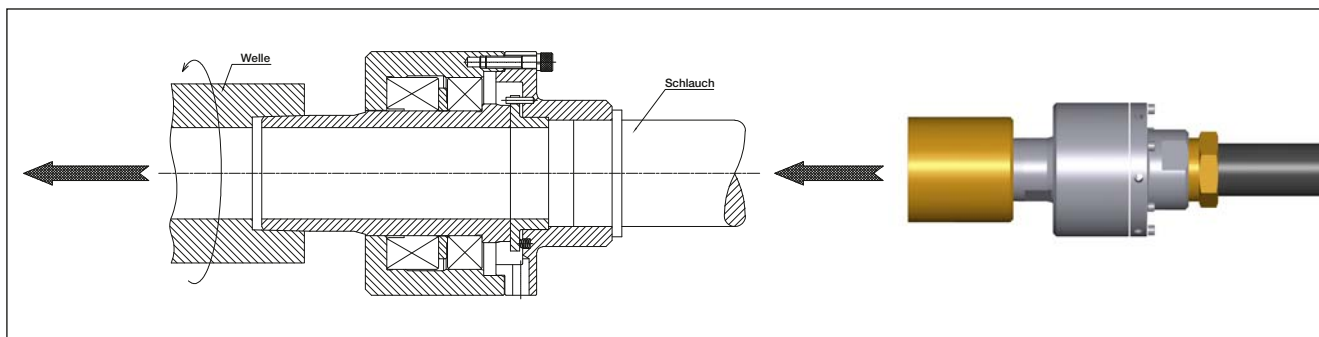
Varianten für die Befestigung an die Maschinenwelle
